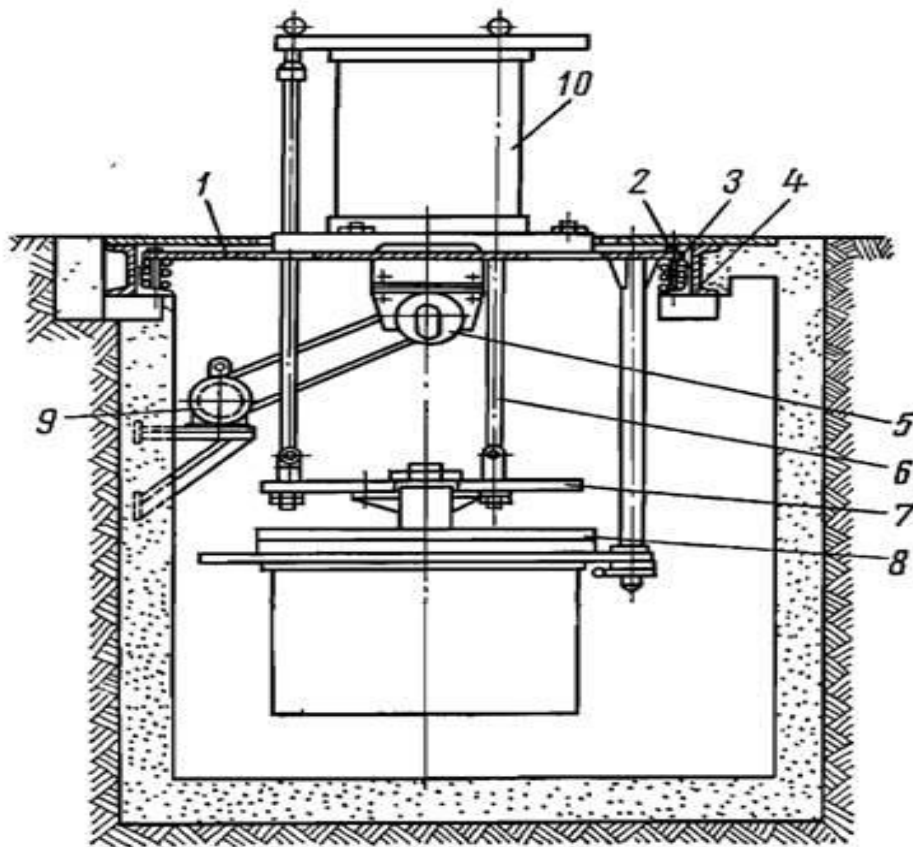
Установка для вибрационной заливки роторов: 1-стол; 2-технологическая оправка; 3-литниковая чаша; 4-верхняя половина формы; 5-разъемная рубашка; 6-сердечник; 7-нижняя часть формы; 8-тяга; 9-подвижная плита; 10-поршень
